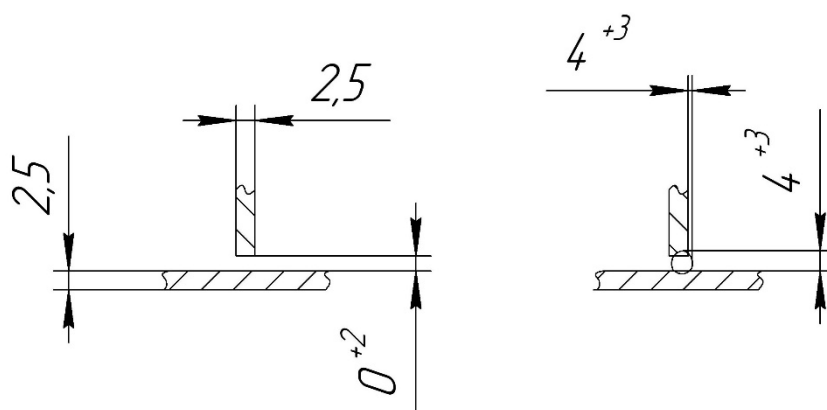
Вид сварного соединения по ГОСТ 14806-80
